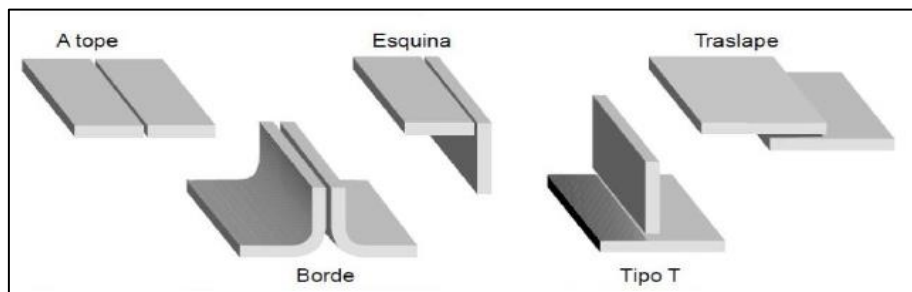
Tipos de uniones más comunes en soldadura
